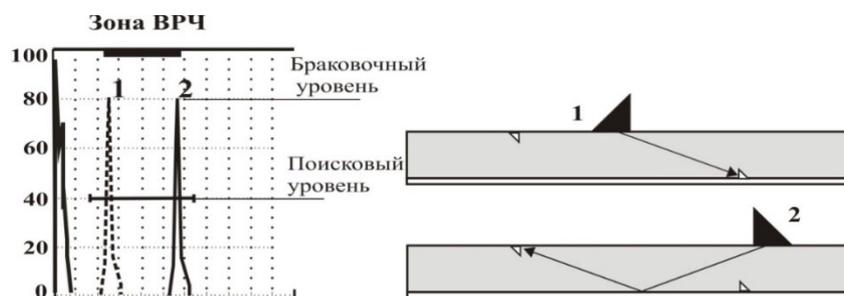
Схема настройки чувствительности при контроле стыковых сварных соединений
